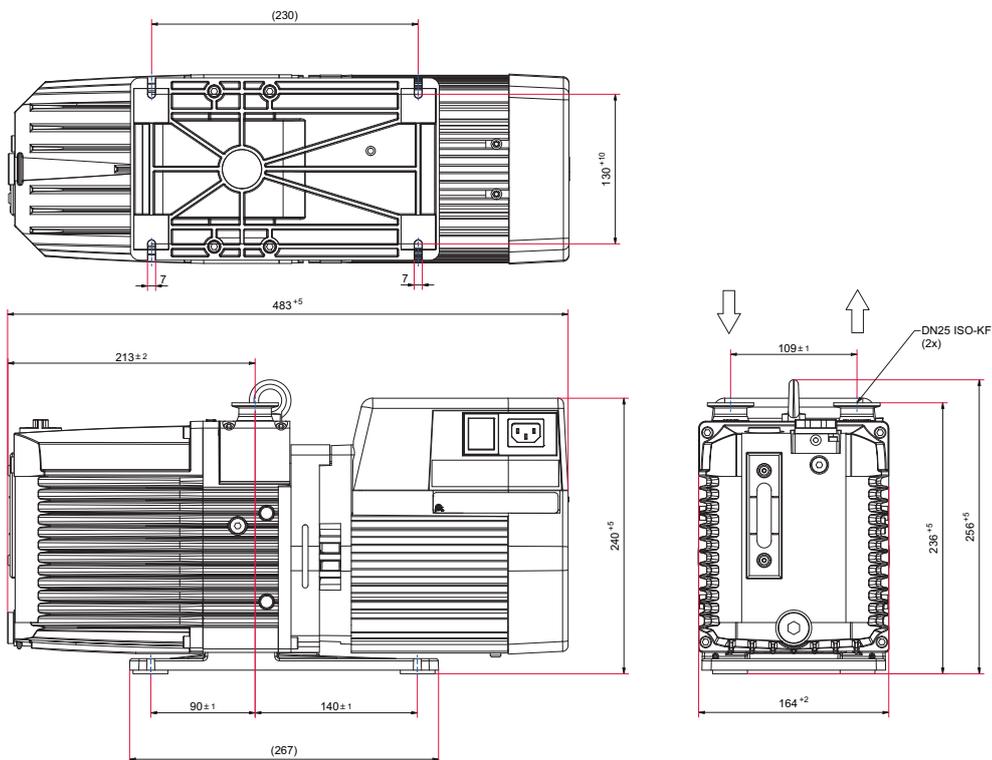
Abmessungen DuoVane 22 mit Einphasenmotor
